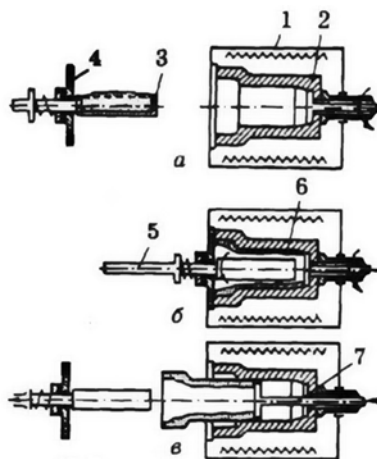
Схема центробежного способа изготовления оболочкового стержня:
